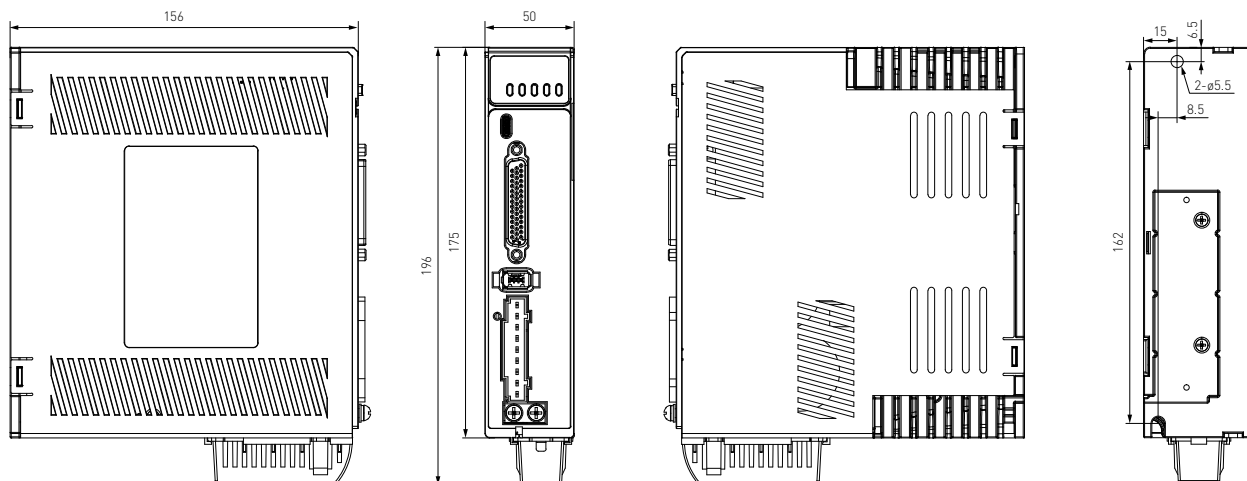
Габаритные размеры драйвера EL7-RS400P.
